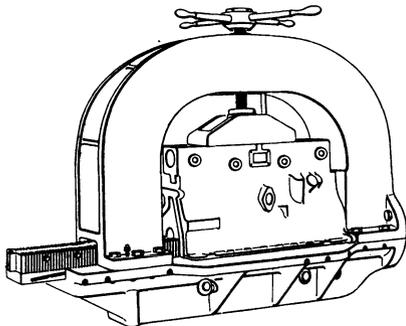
Räumvorrichtung für Zylinderblockbearbeitung auf waagerechter Räummaschine (Forst).
